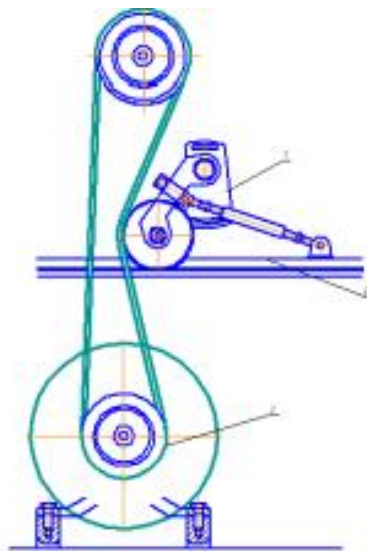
Конструкція ножового приводу: 1 –пристрій натягу; 2 – каток; 3 – двагун
